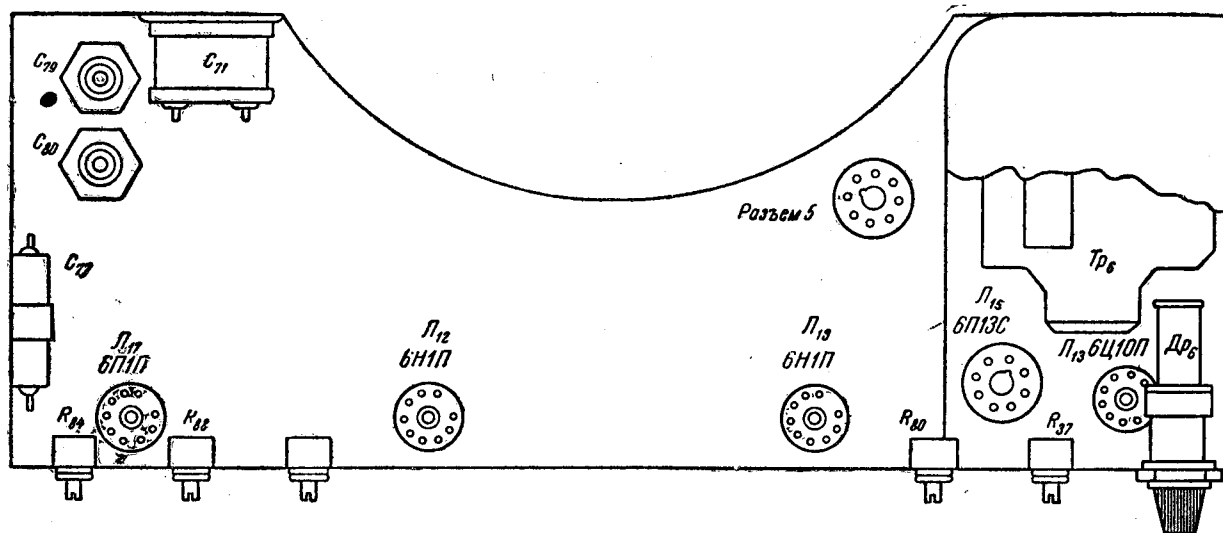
Расположение ламп и деталей блока развертки (вид со стороны монтажа).
